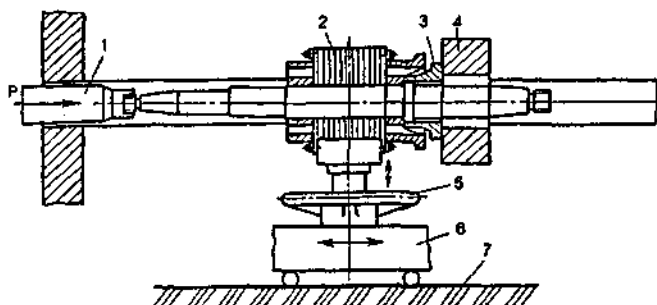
Схема выпрессовки вала из сердечников ротора:
